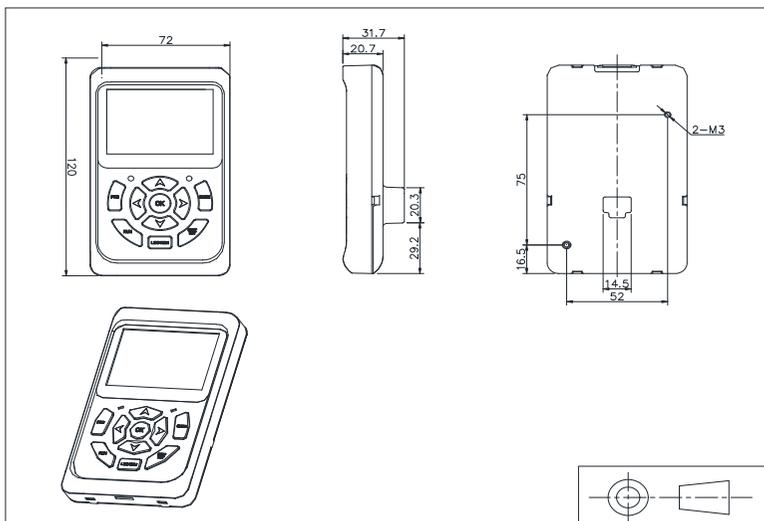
： PI800 键盘尺寸图(尺寸单位：mm)
